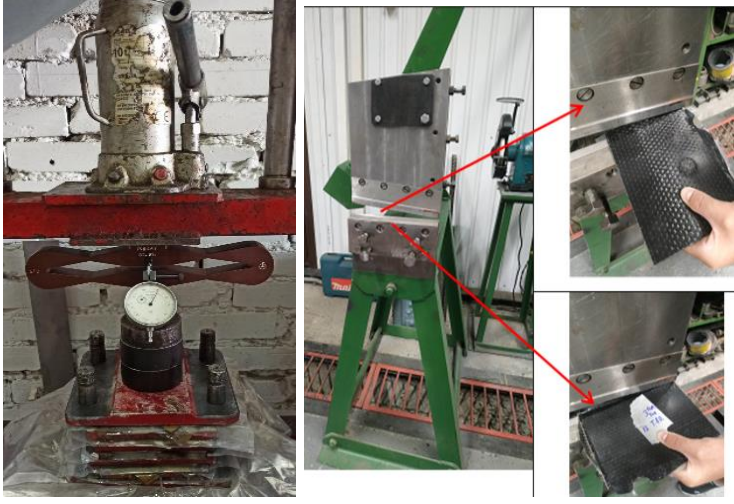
Формовочная оснастка для изготовления образцов из КМ
